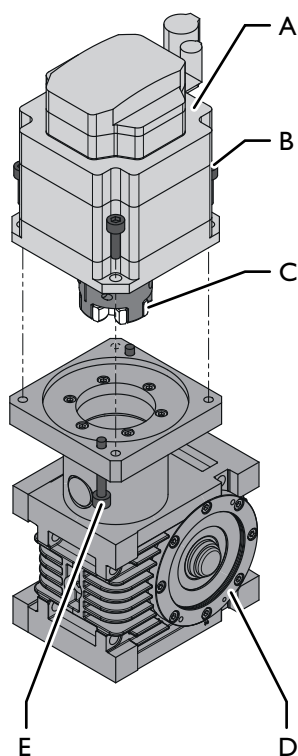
Удалить мотор: Блок редуктора Güdel
